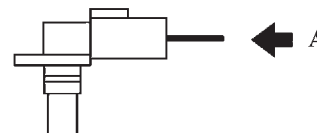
Внешний вид разъема АКП (21902-1700010)
